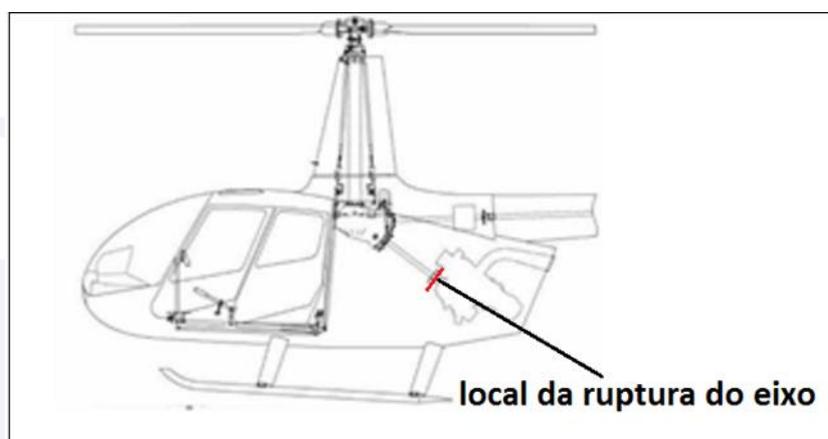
Shaft Weldment* demonstrado no conjunto.
